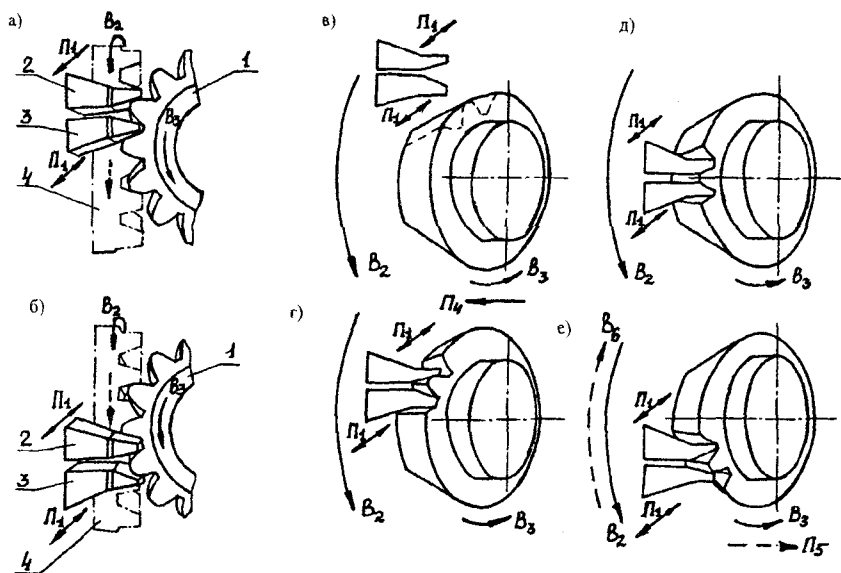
Схема нарезания одного зуба конического прямозубого колеса на зубострогальном станке методом обкатки
